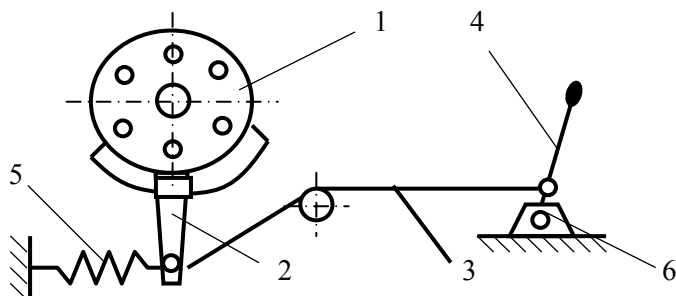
Схема устройства для изменения угла опережения зажигания
